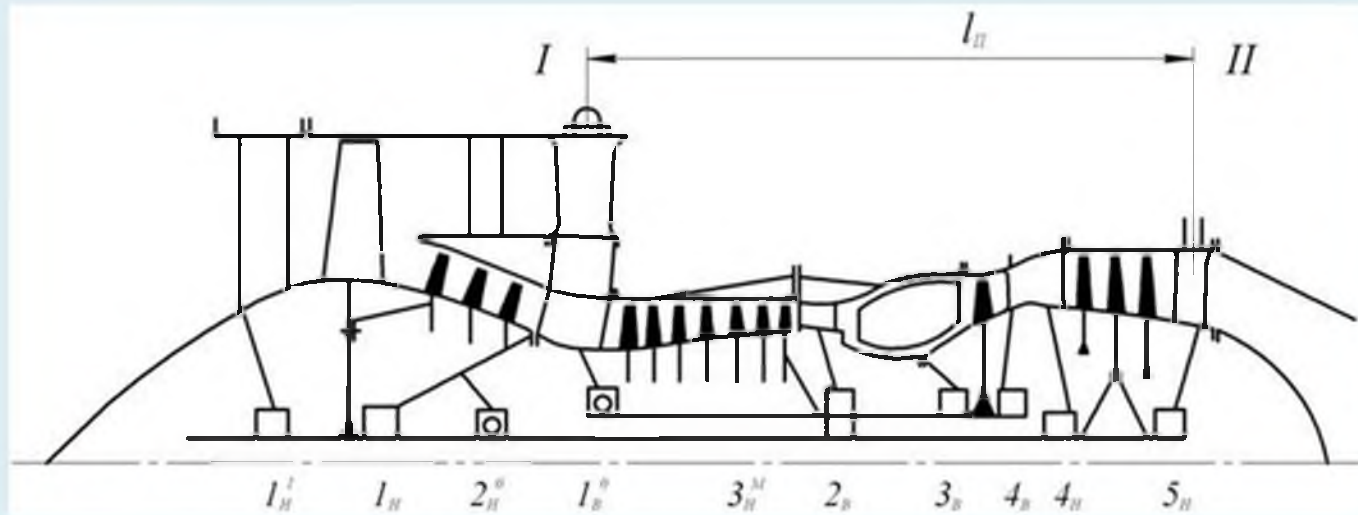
Общая схема размещения и нумерации опор в двухвальвном роторе:
